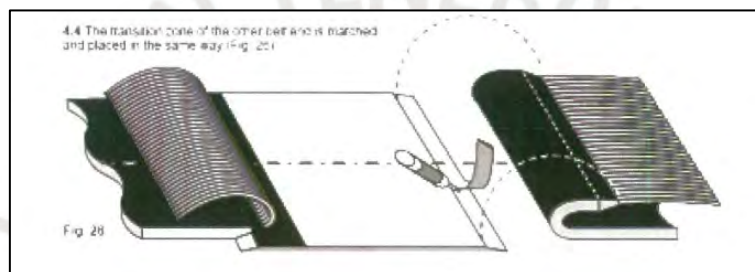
17 Cables descubiertos de las fajas a empalmar.
